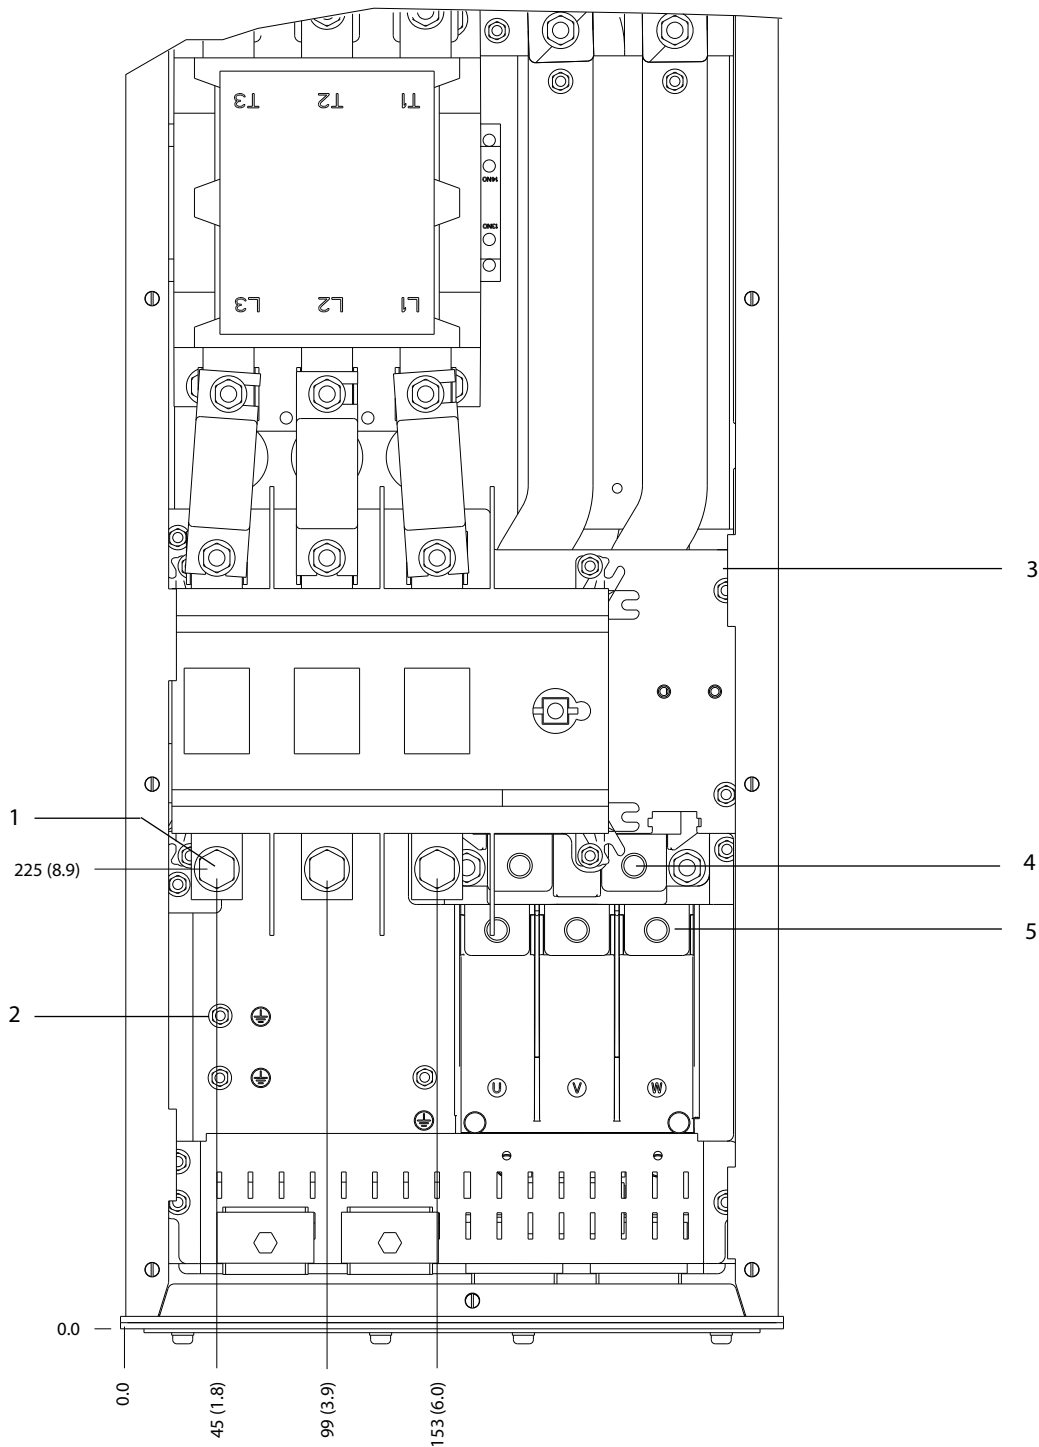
Dimensions des bornes D6h avec option contacteur (vue frontale)
